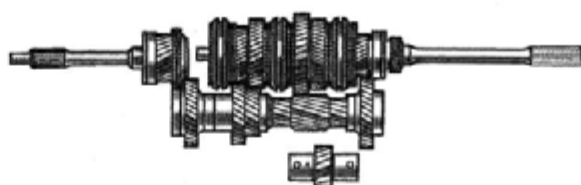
Валы и шестерни коробки передач после их сборки
